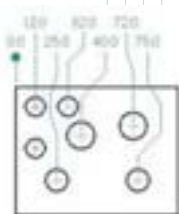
Чтобы обойти препятствия, Solid Edge 12 допускает изломы размерных линий
